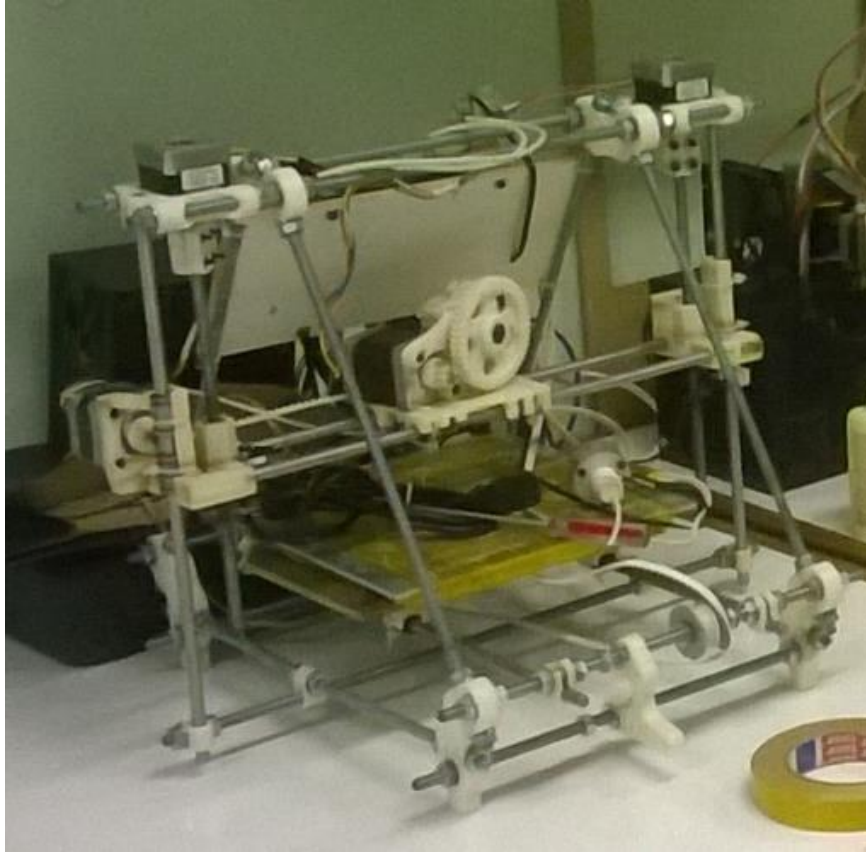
Impressora Reprap Prusa Mendel. Construção por Renan Balzani e Leonardo
